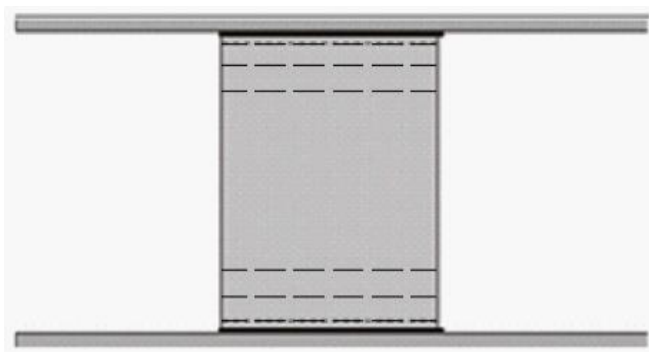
Схема сканирования околошовных зон сварных соединений затяжки клещевого механизма
